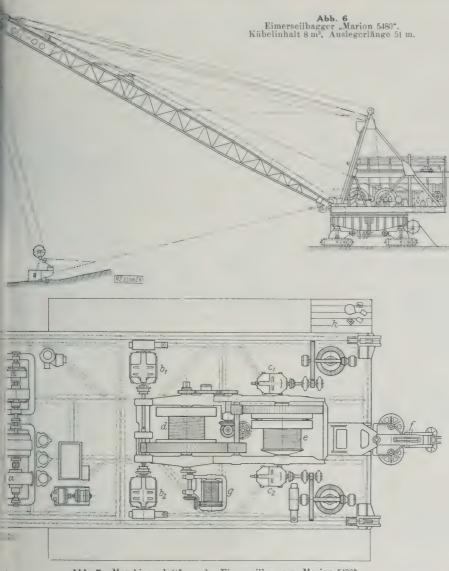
Maschinenplattform des Eimerseilbaggers "Marion 5480". c₁₀ c₂ Drehwerkmotoren e Schürftrommel f Seilführung für Schürfseil maschineuumformer Lubmotoren
